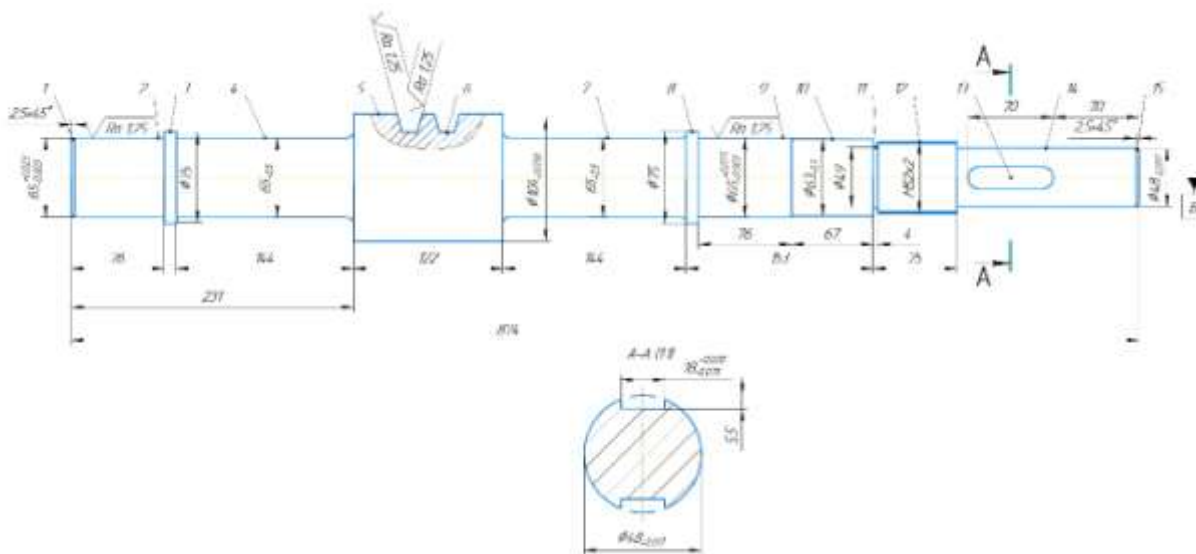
Эскиз детали "Вал червячный " с указанием поверхностей
